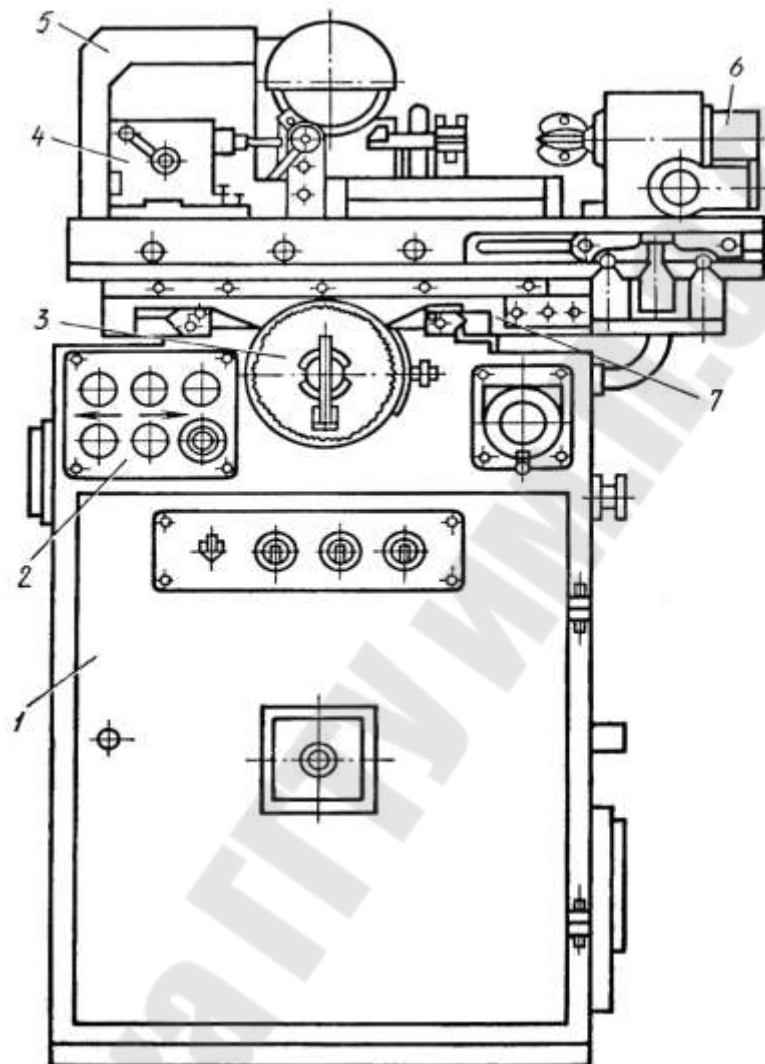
Общий вид полуавтомата модели 3В10М для заточки метчиков по передней поверхности: 1 – станина; 2 – пульт управления; 3 – маховик поперечной подачи; 4 – задняя бабка; 5 – шлифовальная бабка; 6 – передняя бабка; 7 – стол
